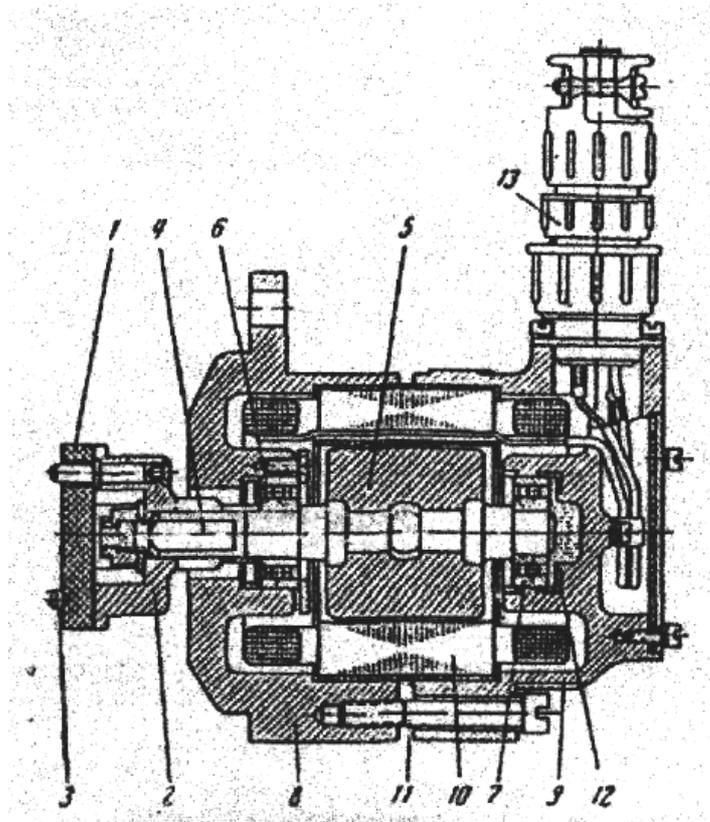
Конструкция синхронного тахогенераторного преобразователя переменного тока: 1 - кожаная прокладка, 2 - фланец, 3 - штифты, 4 - вал, 5 - ротор, 6, 7 - подшипники, 8, 9 - крышки корпуса, 10 - статор, 11 — винты, 12 - обойма, 13 - разъем.
